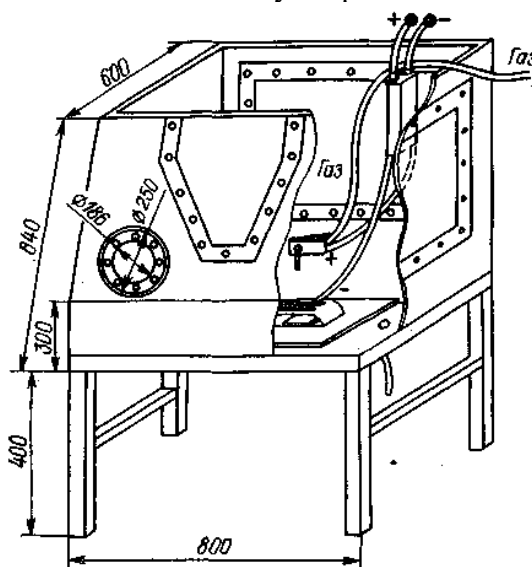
Аквариум для подводной сварки и резки
